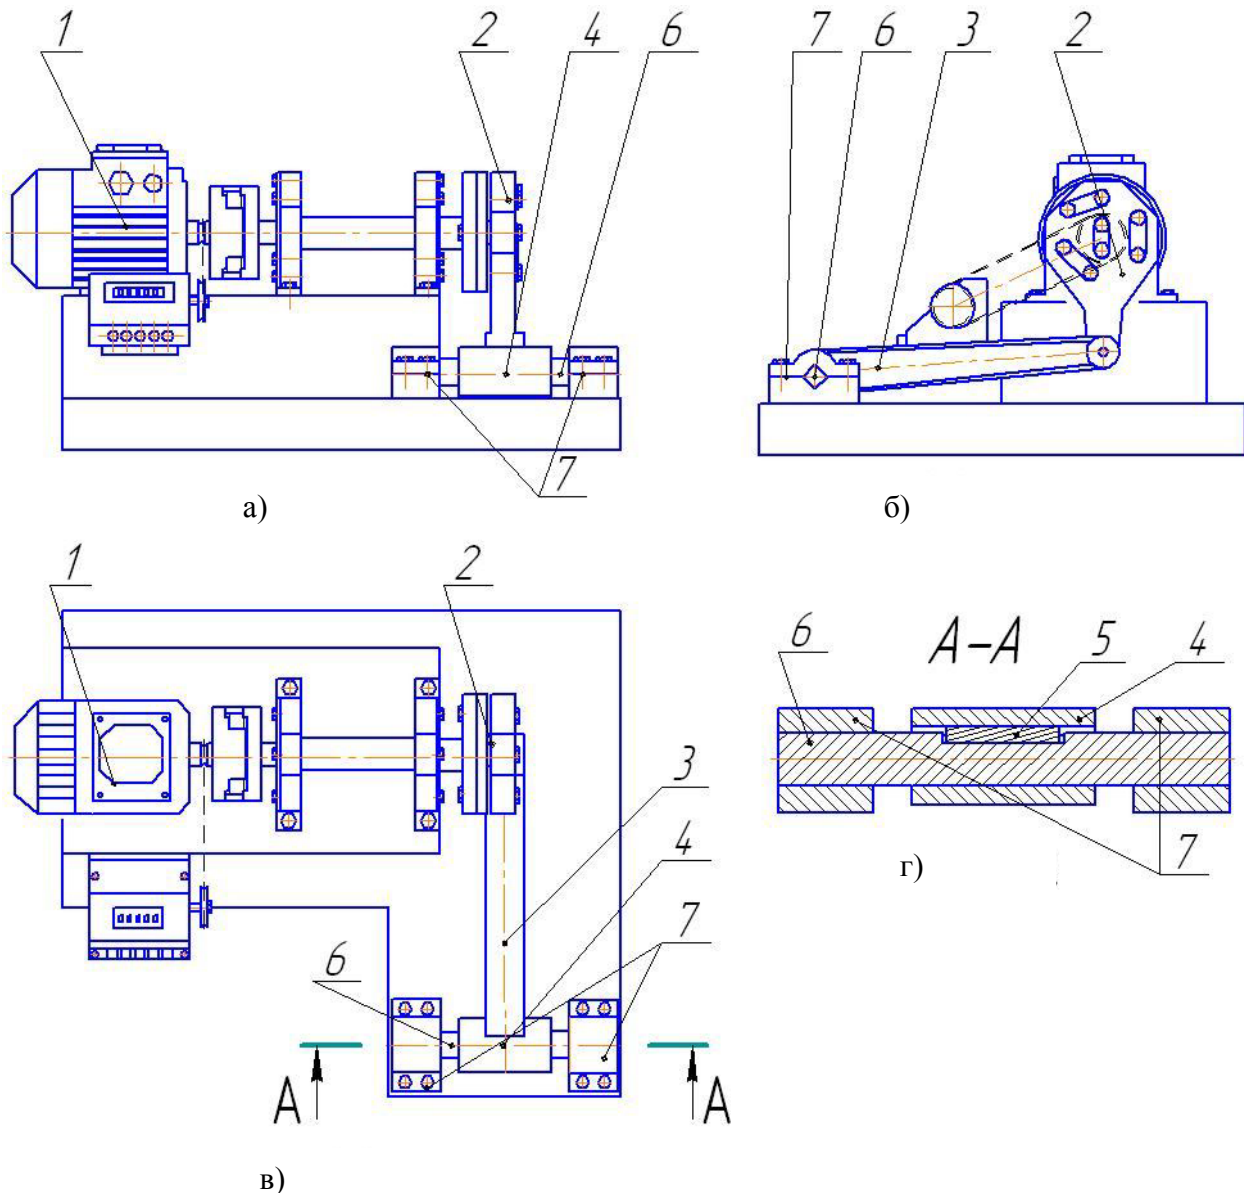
Стенд для дослідження фретингового зношування шпонкових з'єднань.
